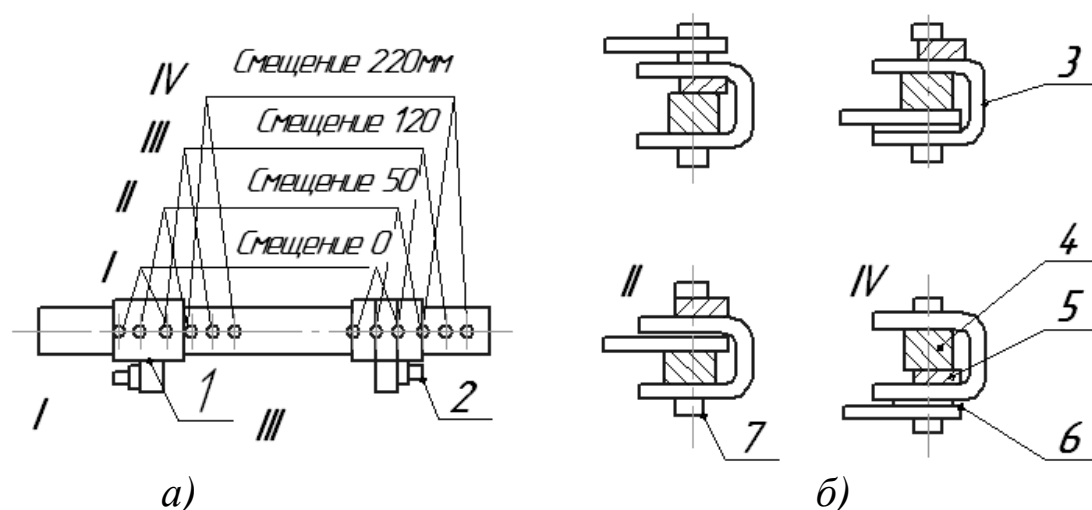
Схемы установки: а) кронштейнов на поперечной балке рамы; б) штока догрузателя
